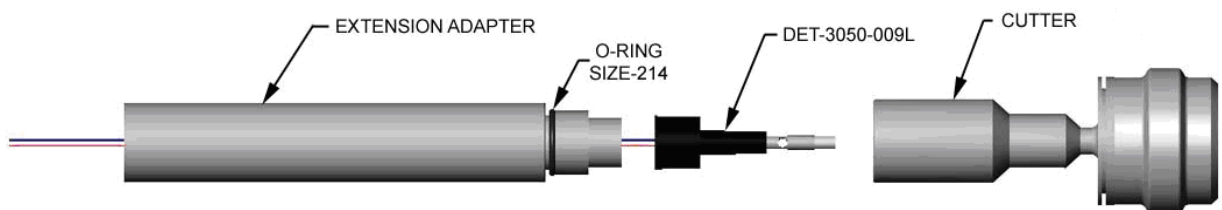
Méthode d'armement des coupe-tubes Super NT Tubing Cutter - Vue éclatée
